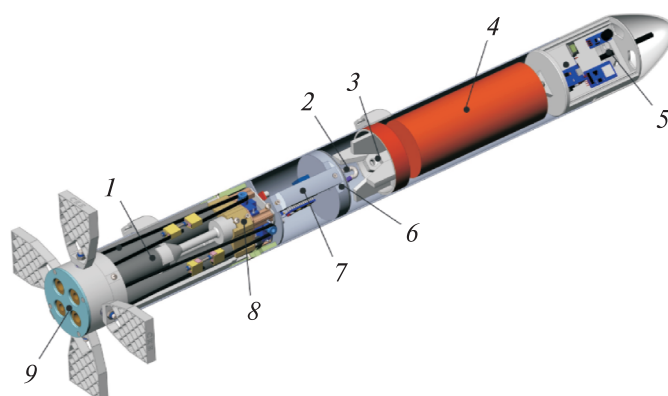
Конструктивно-компоновочная схема летного стенда № 3:
